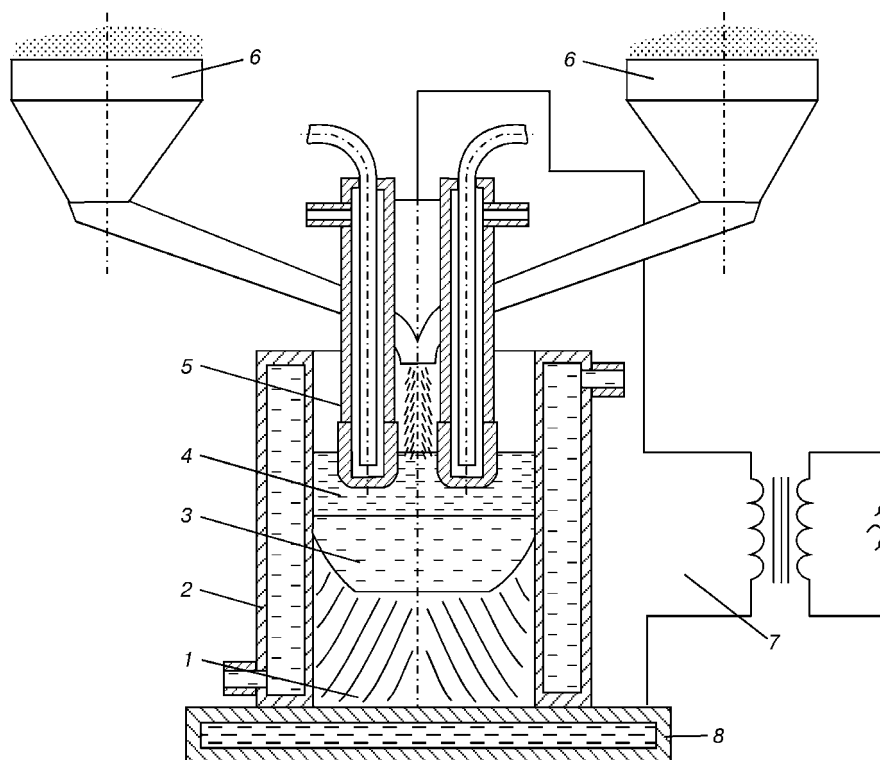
Схема процесса электрошлаковой выплавки ферротитана из титановой и стальной стружки: 1 — твердый металл; 2 — кристаллизатор; 3 — металлическая ванна; 4 — шлаковая ванна; 5 — нерасходуемый электрод; 6 — бункера со стальной и титановой стружкой; 7 — источник питания; 8 — поддон
